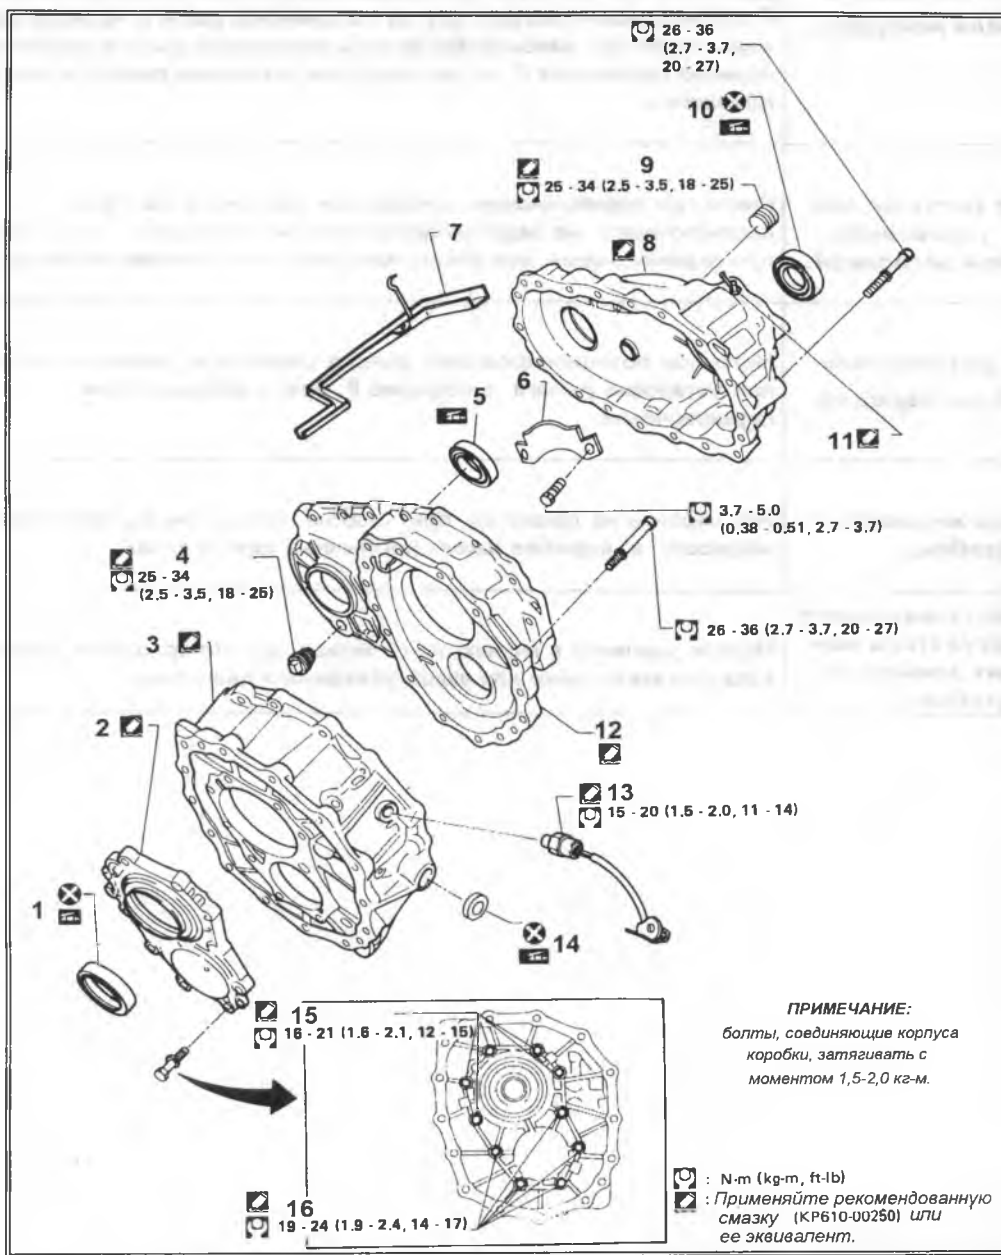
1. Сальник крышки. Повторно не устанавливать. При установке смазать кромки. 2. Крышка переднего корпуса. Перед установкой нанести герметик на поверхность сопряжения с передним корпусом. 3. Передний корпус. При установке нанести герметик на поверхность сопряжения с коробкой передач. 4. Сливная пробка. При установке нанести герметик на резьбу. Момент затяжки 2,5-3,5 кг-м. 5. Сальник центрального корпуса. При установке смазать кромки. 6. Крышка сапуна. 7. Масляный желоб. 8. Задний корпус. При установке нанести герметик на поверхность сопряжения с центральным корпусом. 9. Сливная пробка. Нанести герметик на резьбу при установке. Момент затяжки 2,5-3,5 кг-м. 10. Задний сальник. Не использовать повторно. При установке смазать кромки. 11. Сапун. 12. Центральный корпус. При сборке нанести герметик на сопрягаемые поверхности. 13. Переключатель 4WD. Нанести герметик на резьбу при установке. Момент затяжки 1,5-2,0 кг-м. 14. Сальник вала переключения. Повторно не использовать. При установке смазать кромки. 15. При установке нанести герметик на резьбу. Момент затяжки 1,6-2,1 кг-м. 16. При установке нанести герметик на резьбу. Момент затяжки 1,9-2,4 кг-м.
